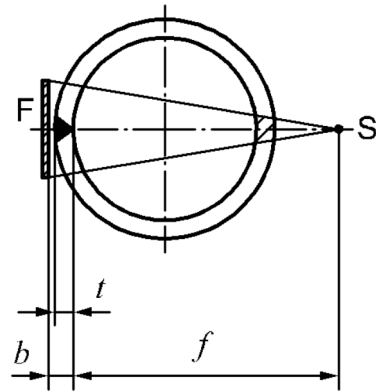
Схема контроля прямолинейного сварного шва при просвечивании через две стенки (одно изображение)
